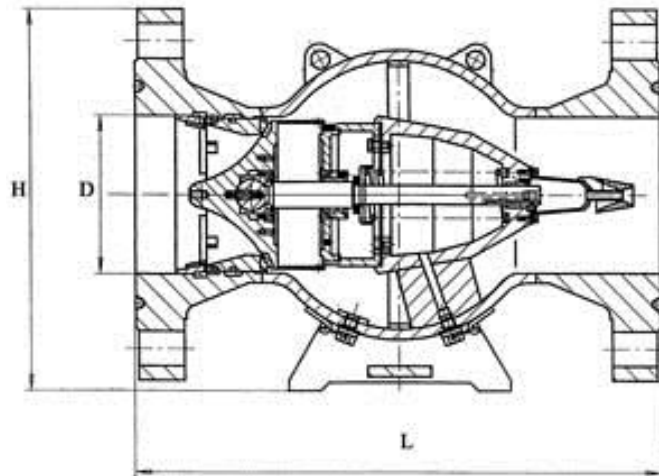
Клапан зворотний безударний К41122-150 під приварювання
